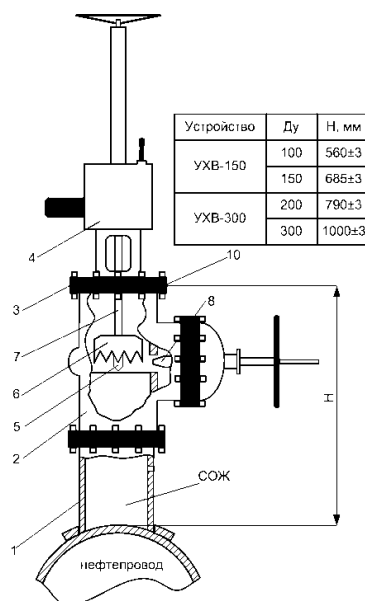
Схема установки устройства на вантуз. 1 – патрубок; 2 – задвижка; 3 – фланец устройства; 4 – устройство УХВ; 5 – сверло; 6 – фреза; 7 – шпиндель; 8 – клин задвижки; 10 – фланец задвижки.
